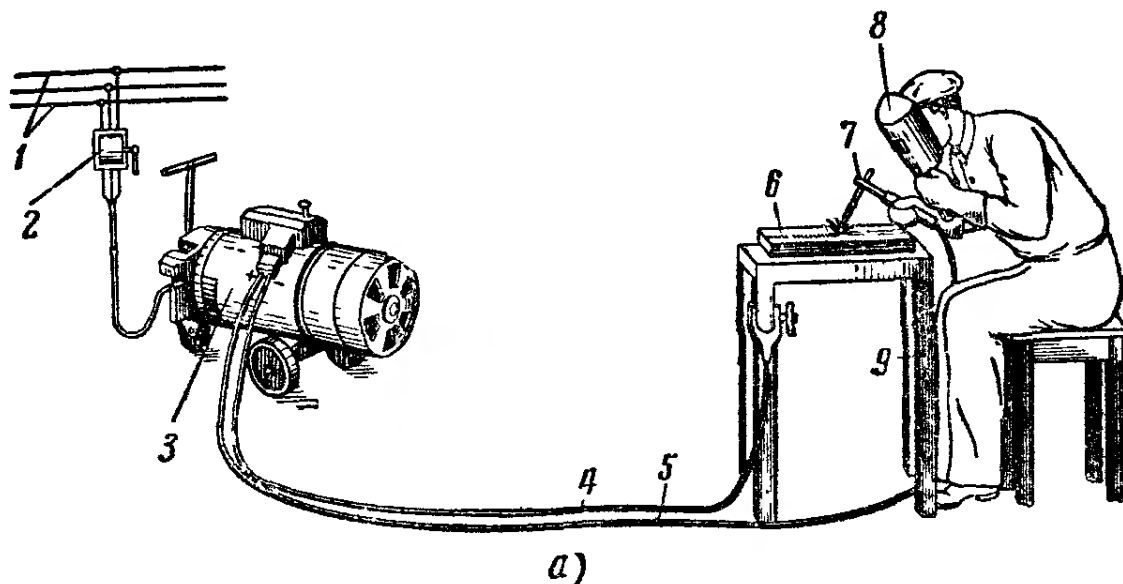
Сварочные посты для ручной дуговой сварки:
